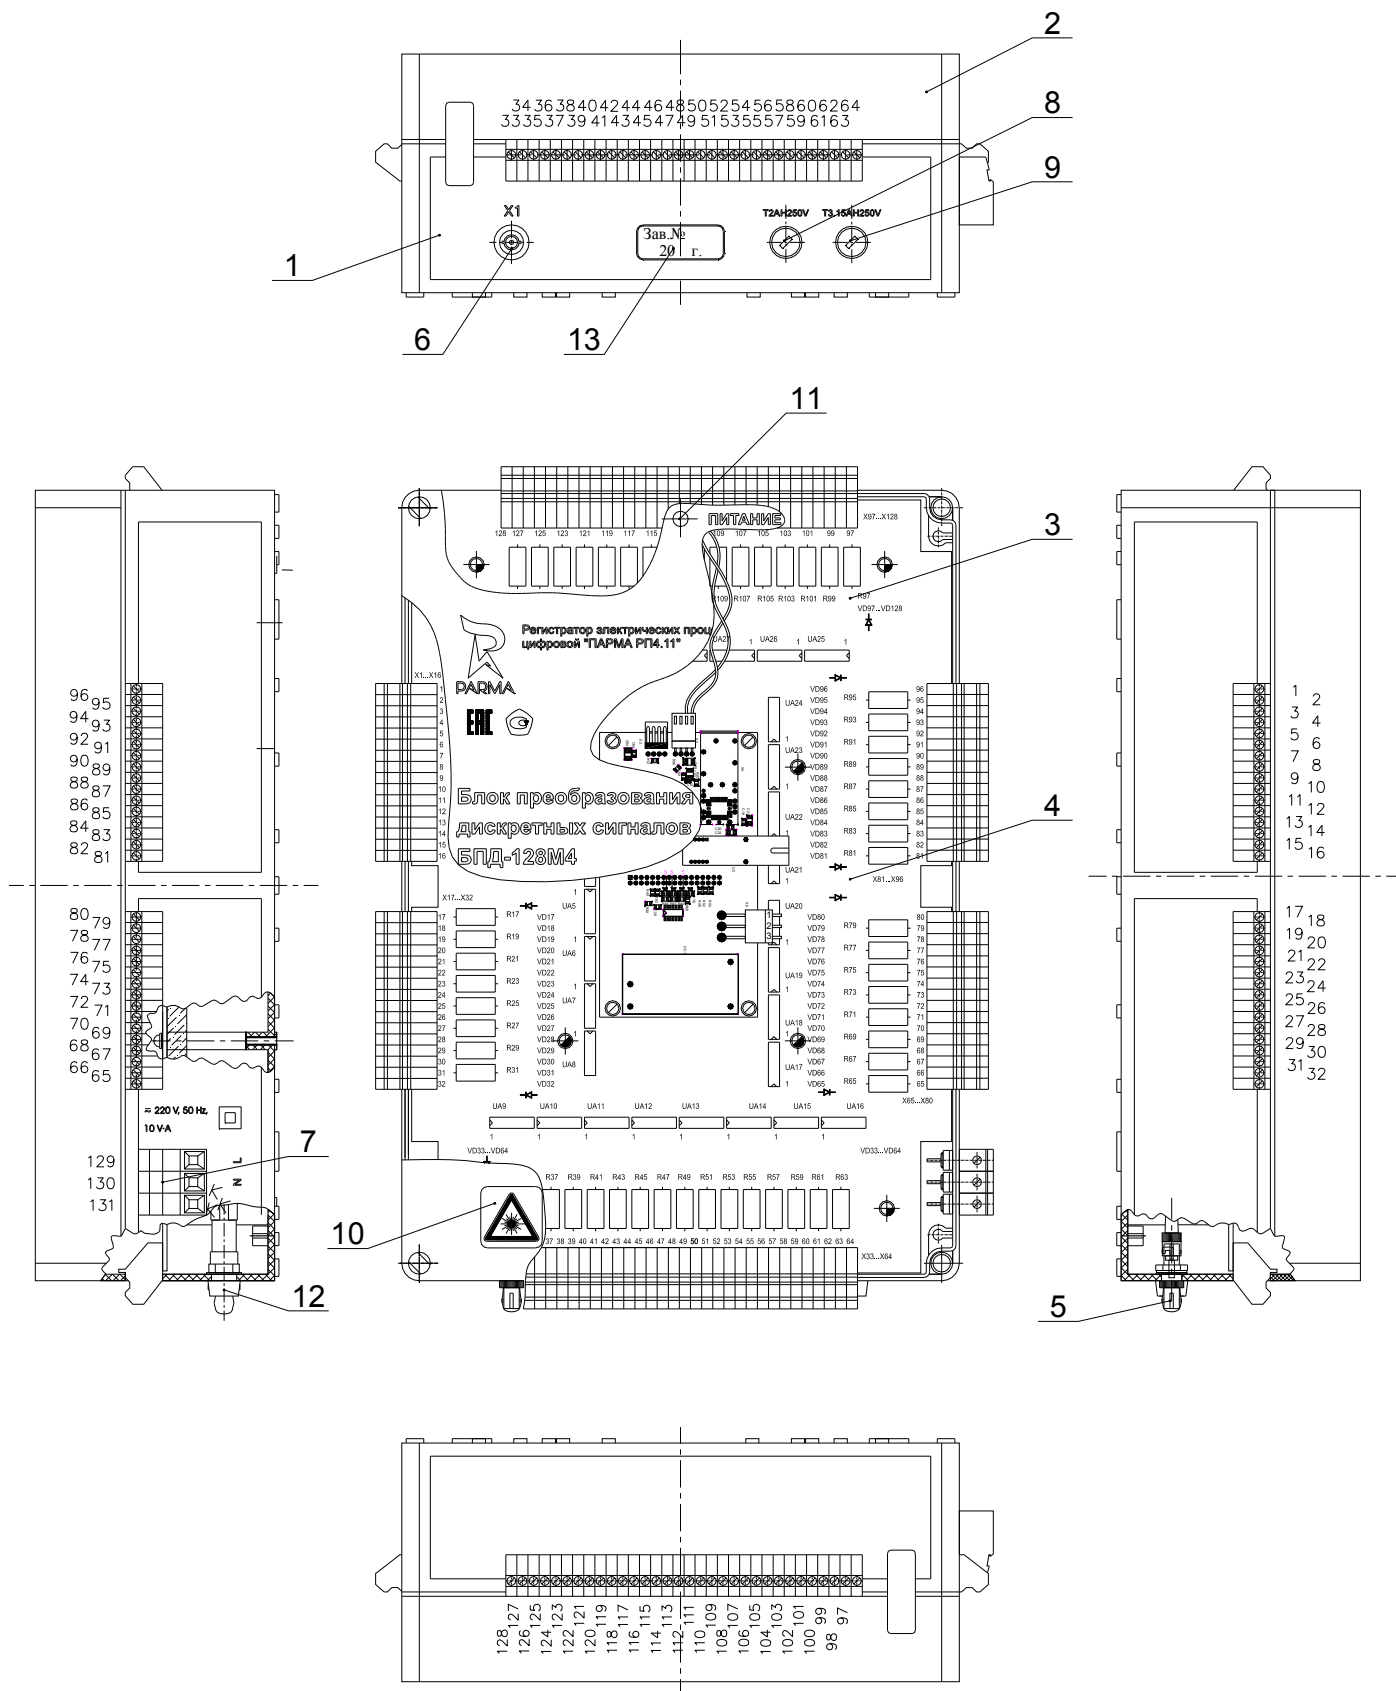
Внешний вид и устройство блока БПД-128М4
